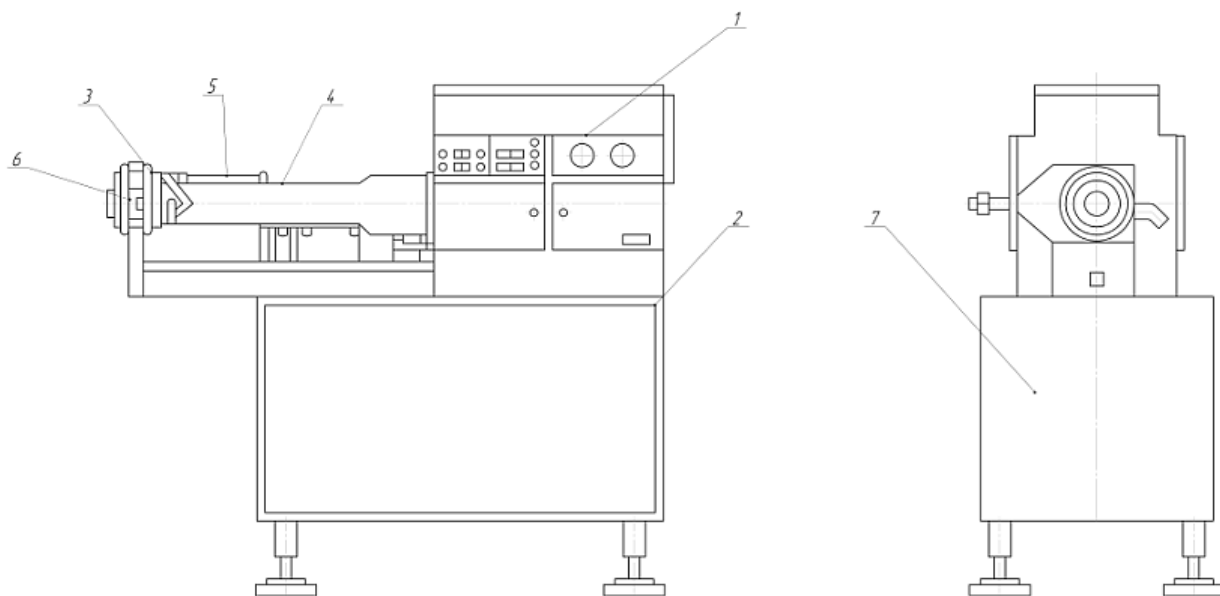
Загальний вигляд преса дообвалочного Mainca K-25.14
